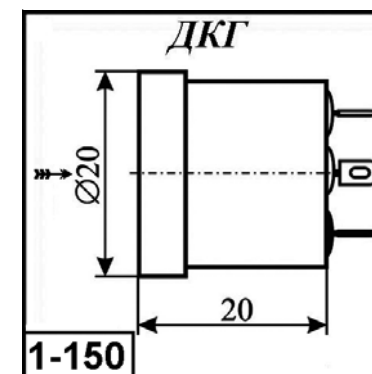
Внешний вид и габаритные размеры детектора типа ДКГ.
